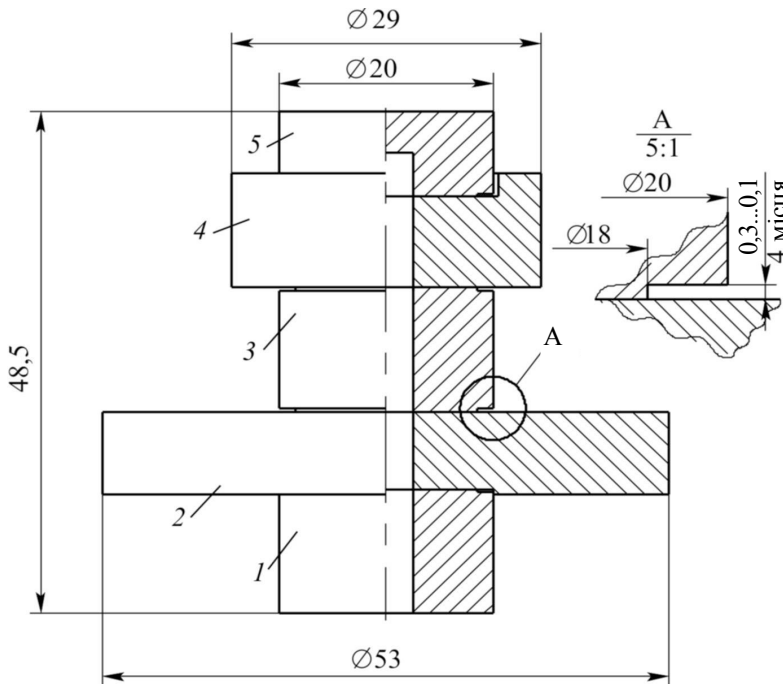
Заготовки корпусу електромагнітного клапана, складені для ДЗВ
